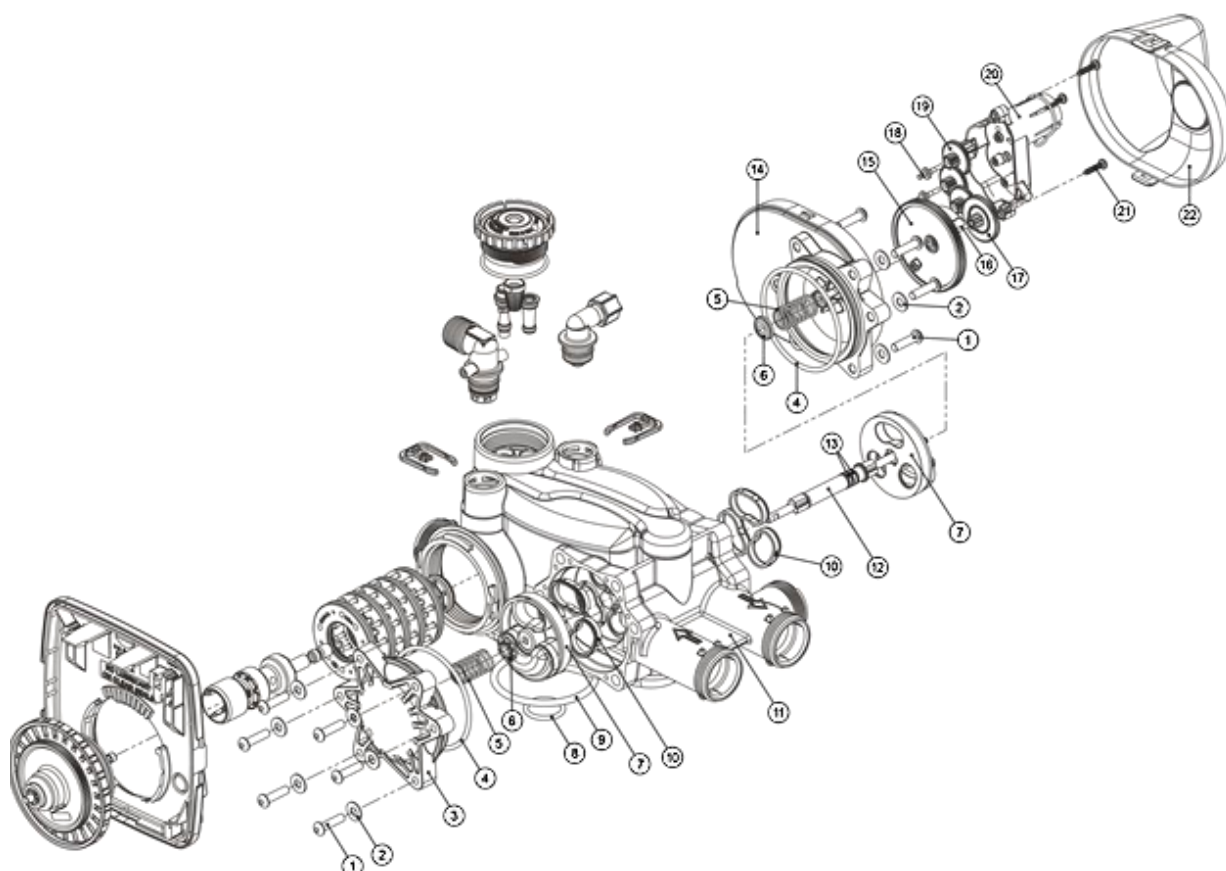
Ersatzteile für Steuerventil WS 1 CI Twin-Twin
